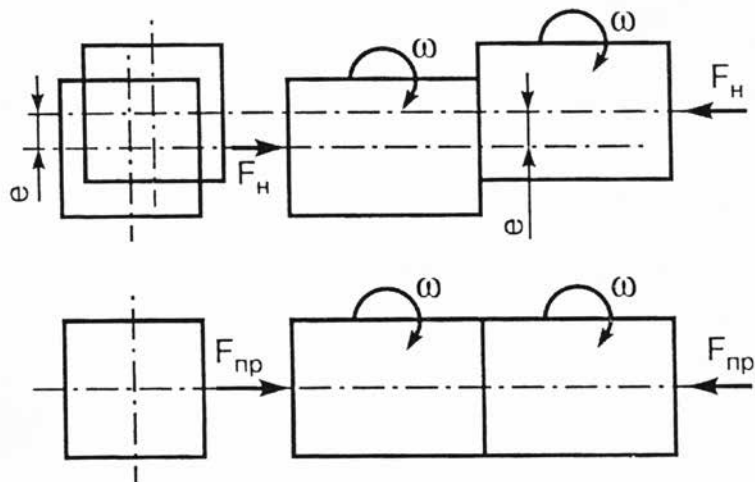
Схема орбитальной СТ: а – стадия нагрева; б – стадия проковки
